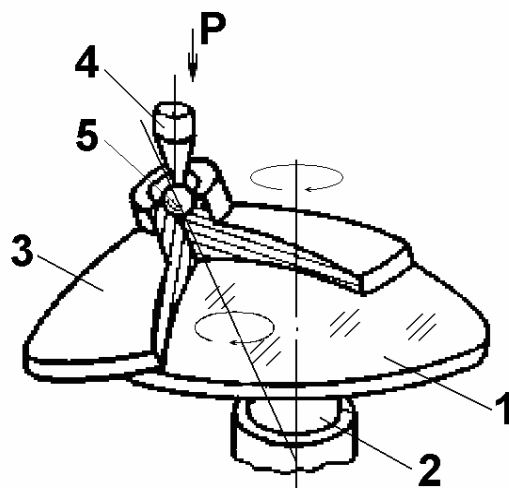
Схема поверхневого притирання у вигляді металевої чашки з вільним абразивом
